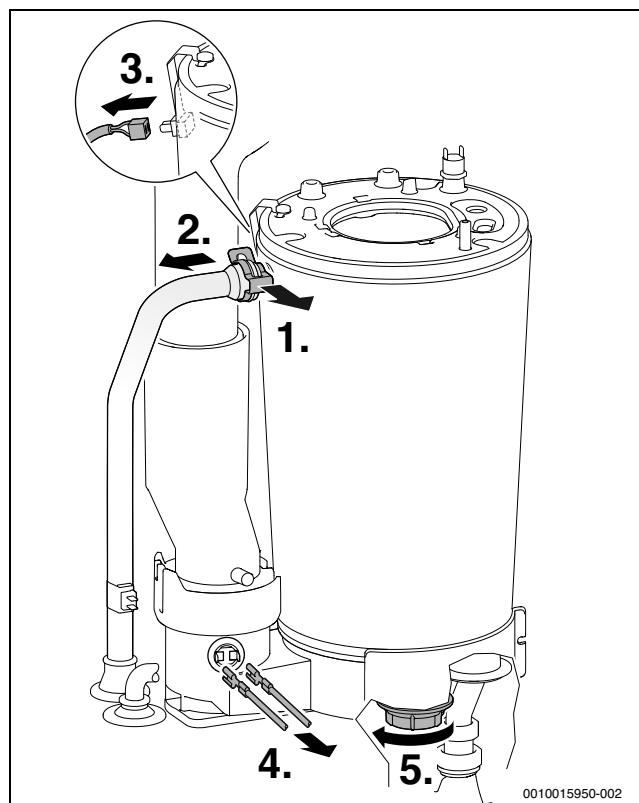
Soltar o tubo de avanço e retirar o cabo
